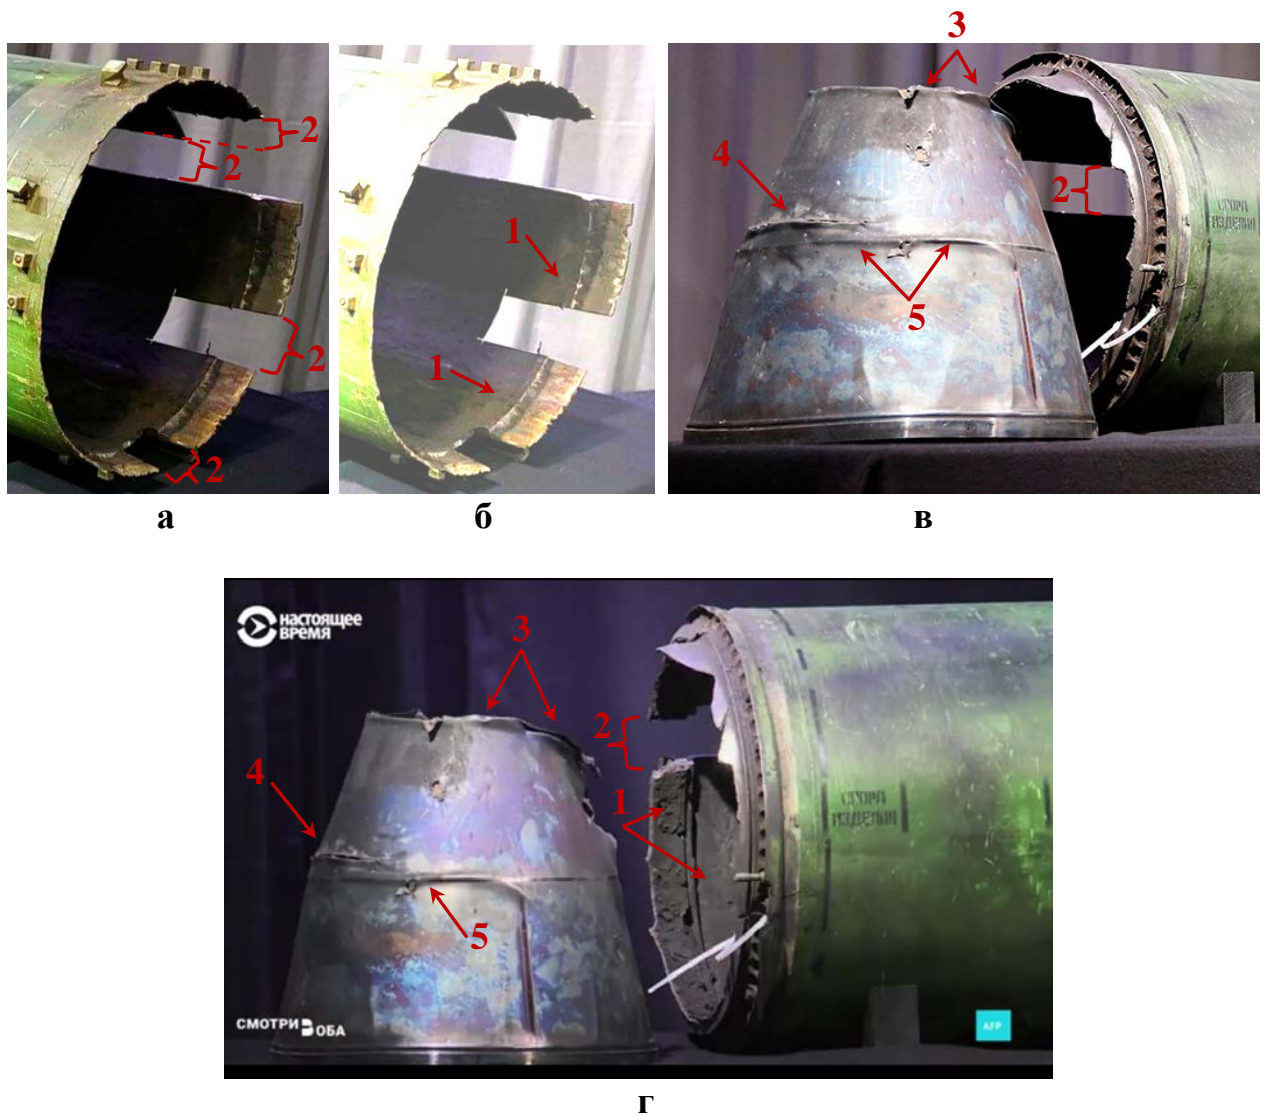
Фотографии фрагментов корпуса и сопла, на которых признаков работы двигателя нет. а – фотография передней части корпуса двигателя, вырезанная с фотографии на рис. 56. б – фотография «а» с добавленной яркостью в графическом редакторе. Стрелками 1 указаны места, где следовало ожидать появления признаков горения топлива. 2 – места вырезки из корпуса образцов. 3 – деформация кромки излома наружу. 4 – трещина с отгибом краёв наружу. 5 – гофр (вспучивание) поперечного сварного шва от нагрузки на сжатие
